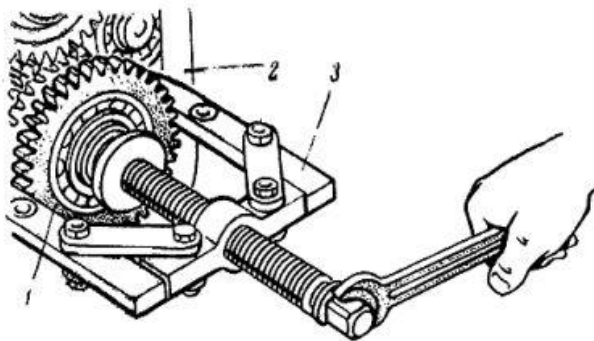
Выпрессовка промежуточной шестерни понижающего редуктора: 1 - шестерня; 2 - корпус КПП; 3 - съемник
